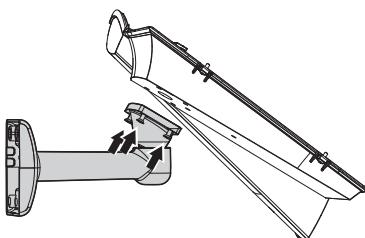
Befestigung auf der Halterung mit interner Kabeldurchführung
